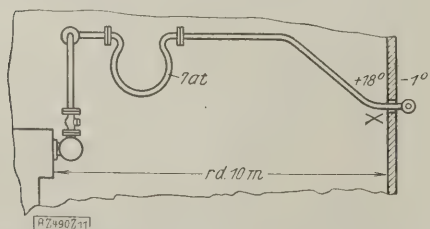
Rohrplan einer von einer Explosion heimgesuchten Kompressoranlage.
